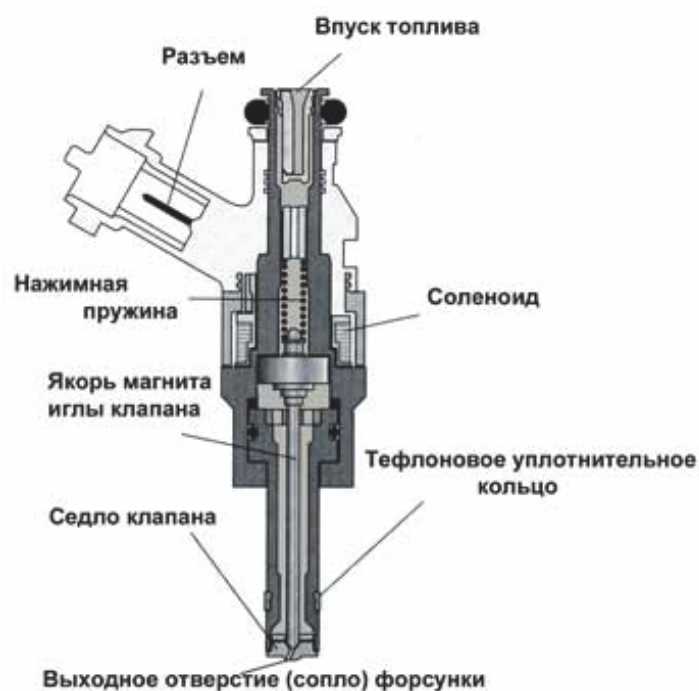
Форсунка высокого давления двигателя системы FSI [6]
